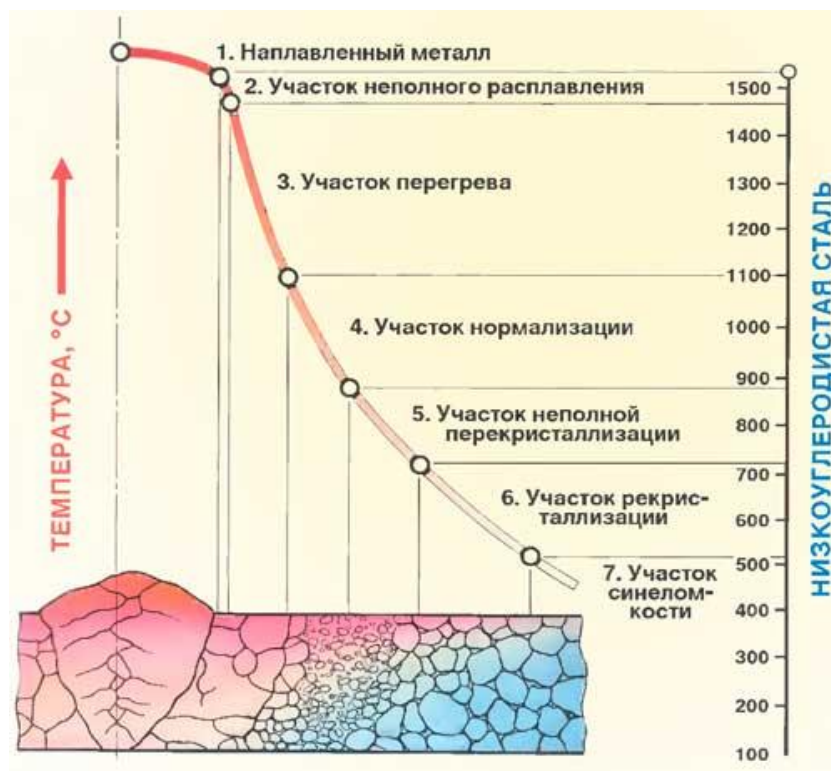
Структура сварного соединения, полученного методом дуговой сварки
